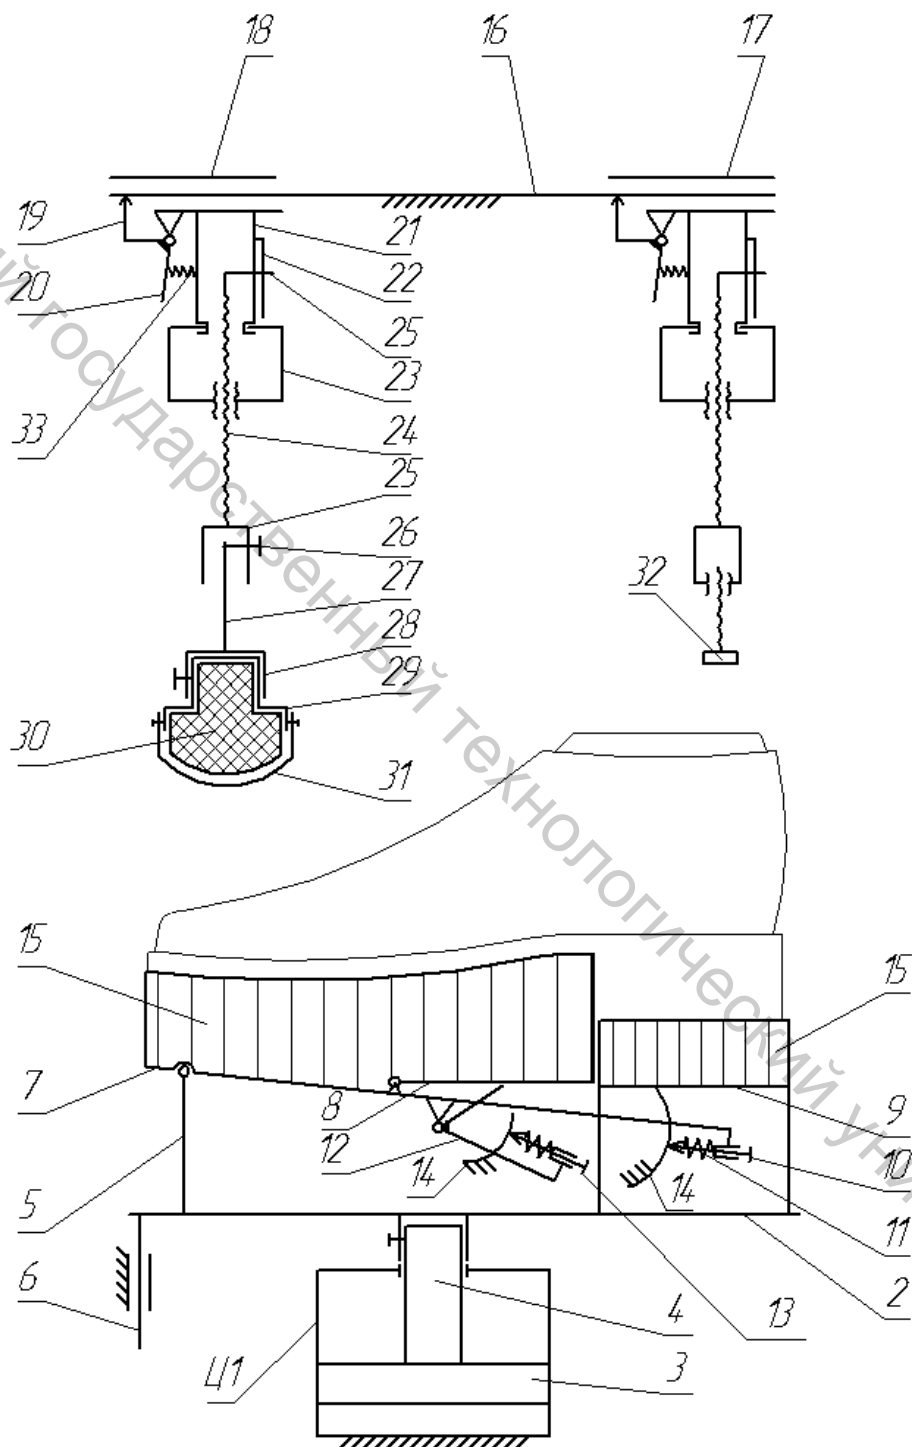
Кинематическая схема механизмов пресс-подушки и упоров
